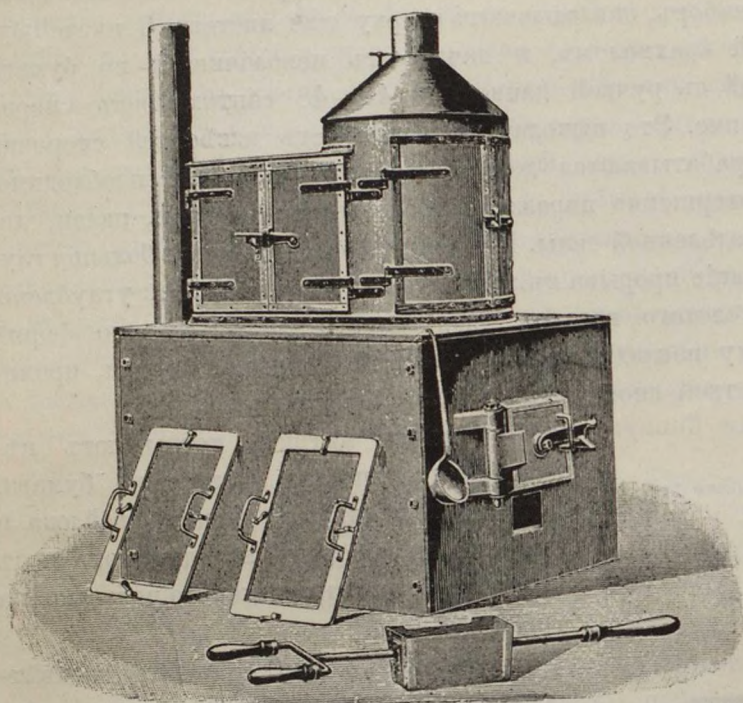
Очагъ для плавленія гарта и сушильный шкапъ. Внизу двѣ рамки для зажиманія матрицъ; на очагъ виситъ ложка для черпанія металла и внизу особой формы котелокъ съ ручейками для наливанія въ него расплавленного гарта.
